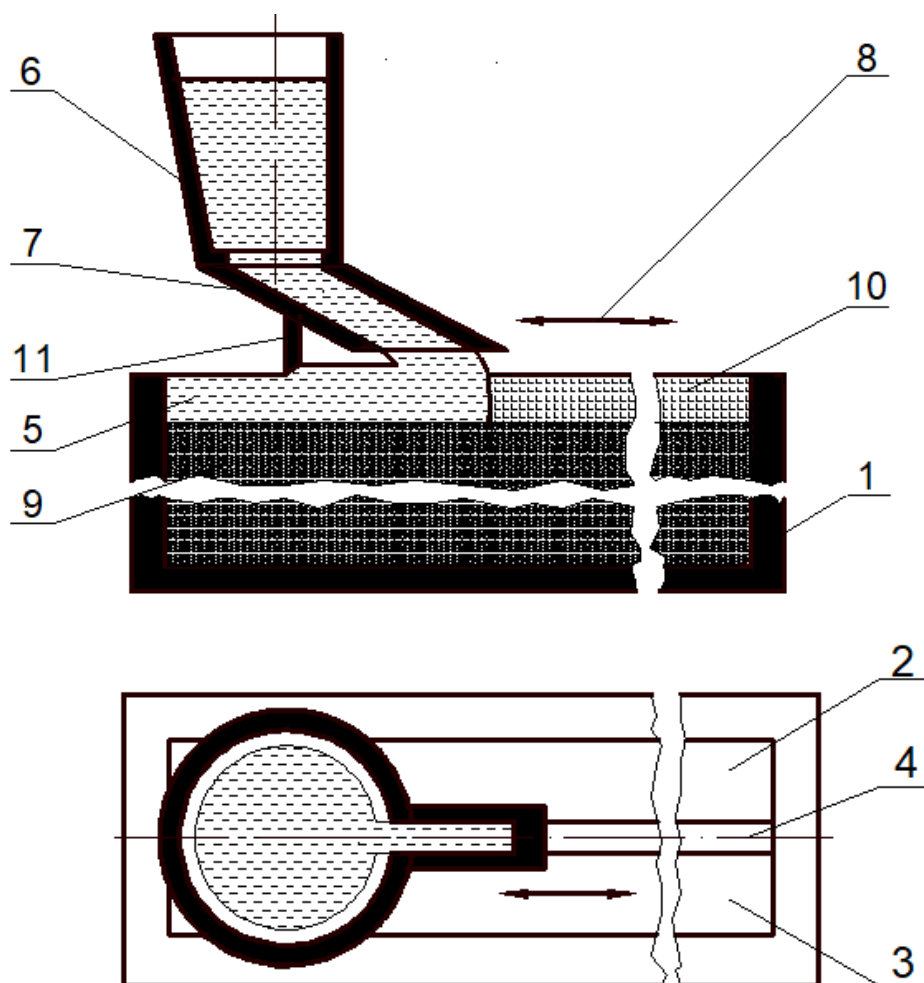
Спосіб виготовлення біметалів зі зчепленням його пластин при заливці рідким металом між вертикально встановленими пластинами біметалу
